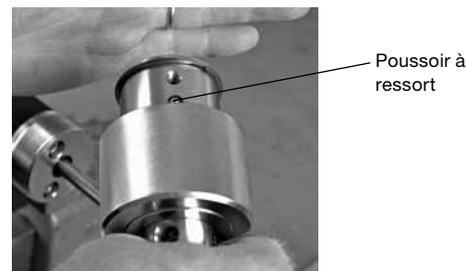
Exposer l'extrémité de l'outil à usiner des cônes
